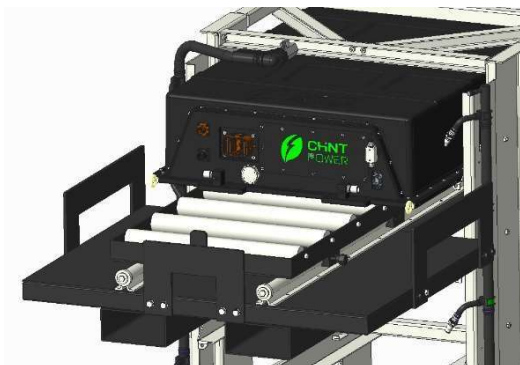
16 Coloque el paquete de baterías en la herramienta de elevación
